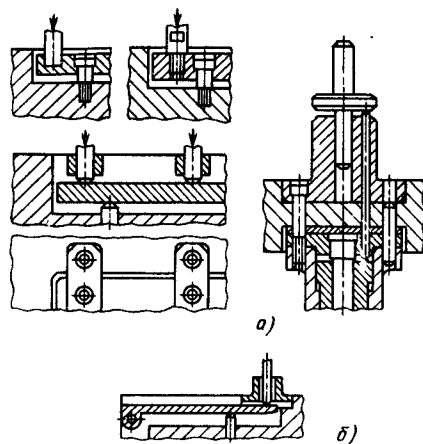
Разновидности способов связи верхнего толкателя пресса со штампом
